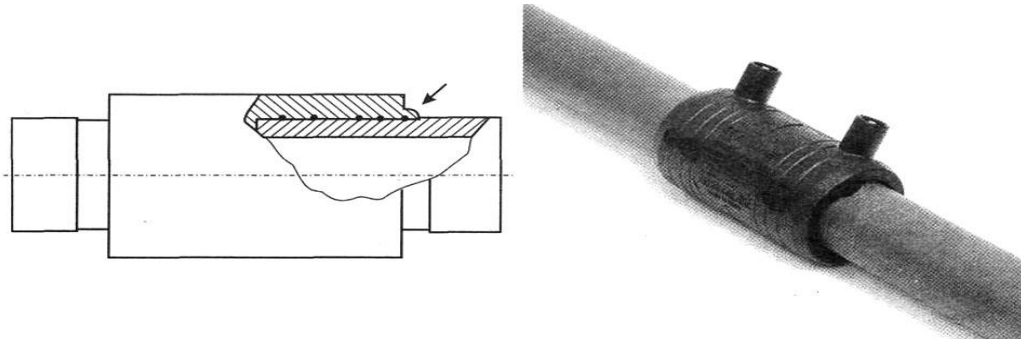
Некачественно выполненное сварное соединение с ЗН (появление расплава полиэтилена по торцу)
